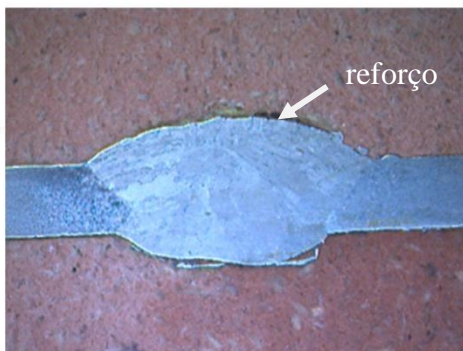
Macroestruturas das juntas soldadas para cada condição avaliada
